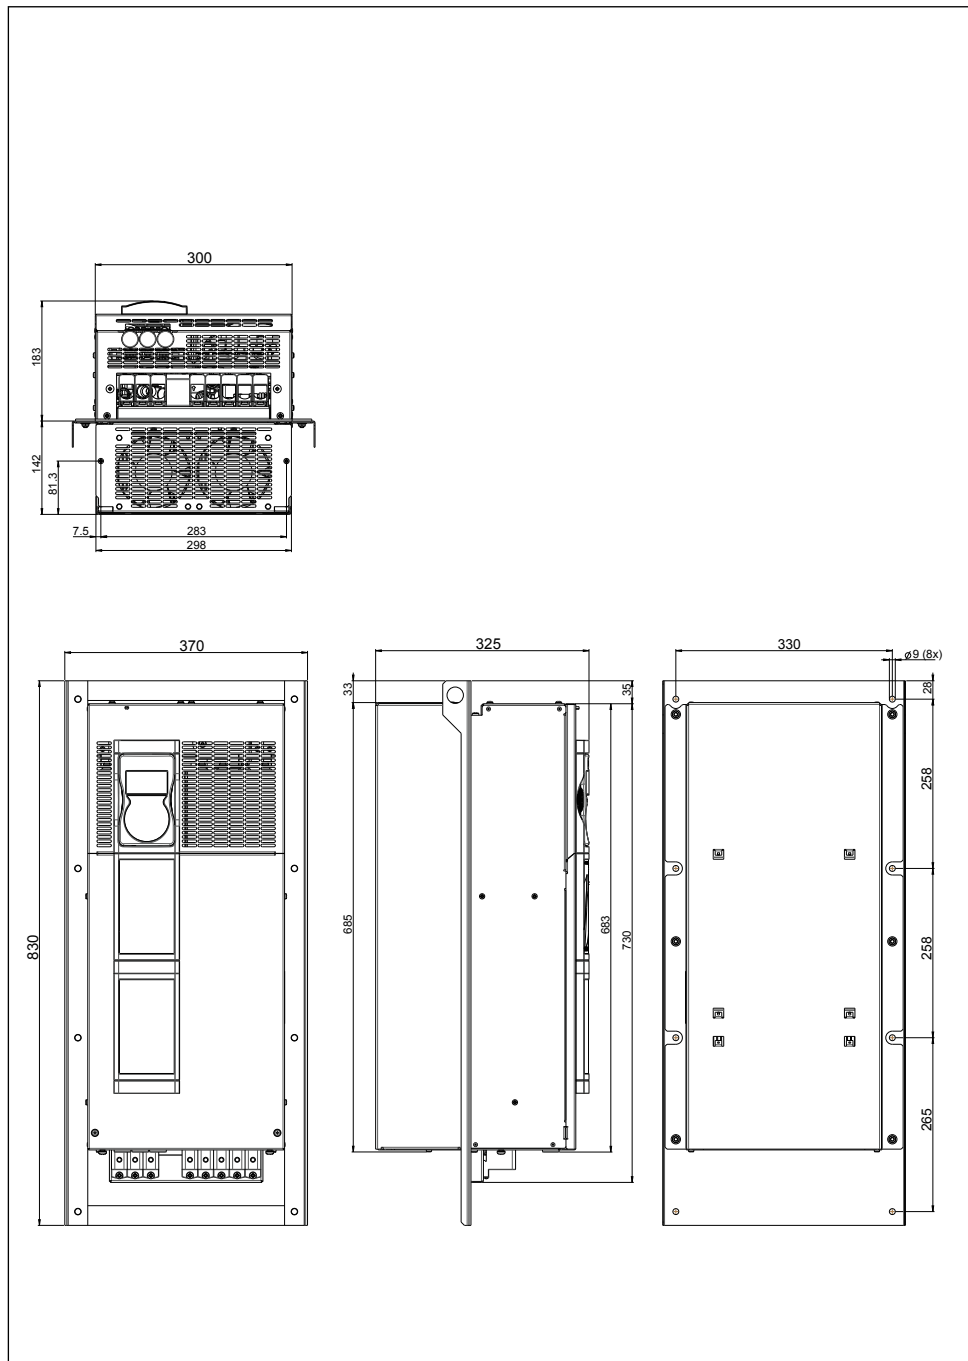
Размеры для типоразмера 6 (ADV200-...-EH)
